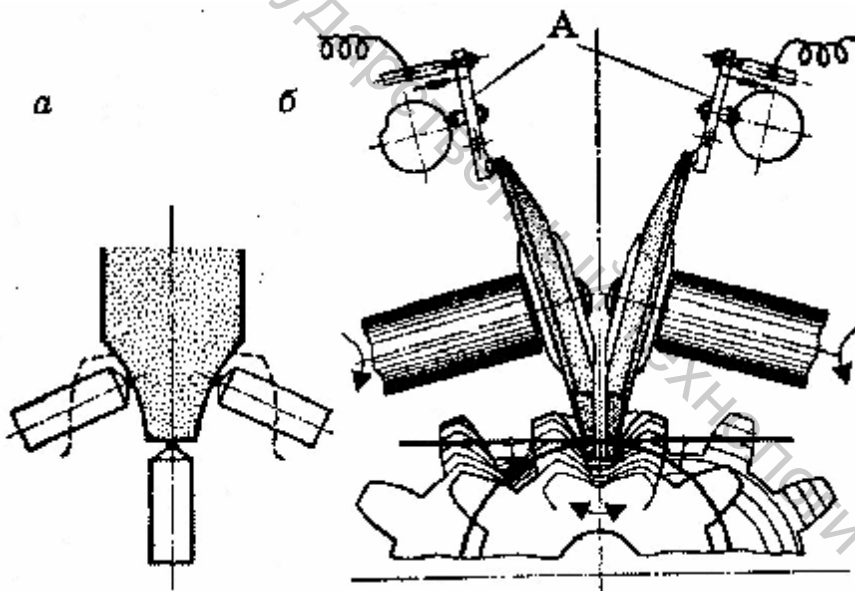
Зубошлифование: а — заправка тремя алмазами профиля шлифовального круга, работающего методом копирования; б — обработка двумя тарельчатыми шлифовальными кругами методом обкатывания
